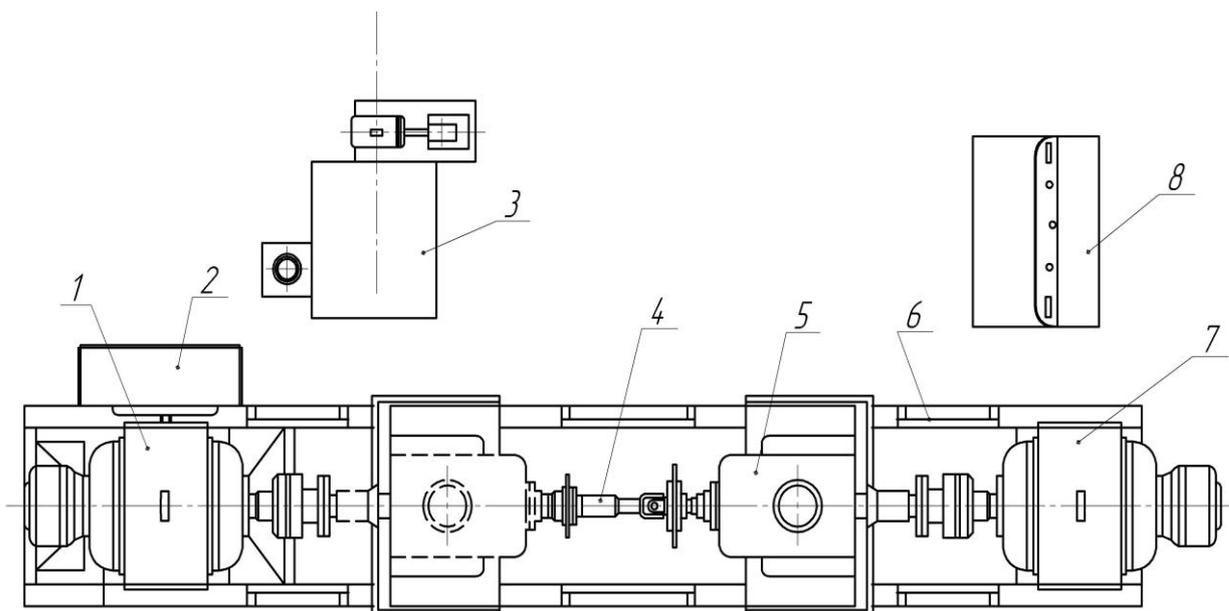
Стенд для испытания коробок передач, модель 6101-11
